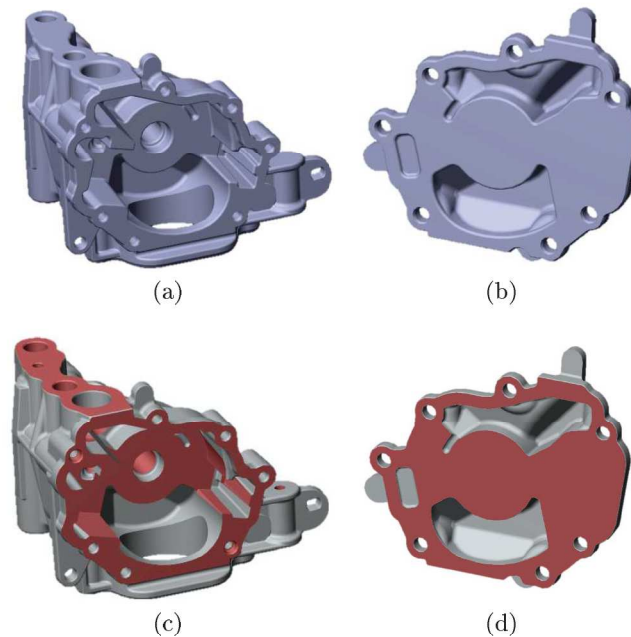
a) Corpo bruto; b) Corpo maquinado; c) Tampa bruto; d) Tampa maquinado.
